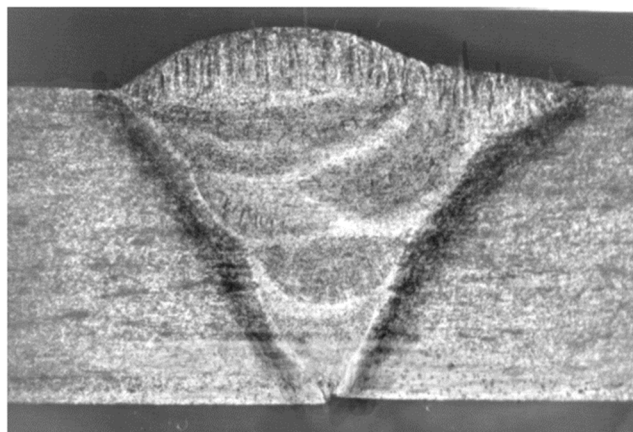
Mehrlagenschweißung, geätzt mit Heyn¹¹⁸
